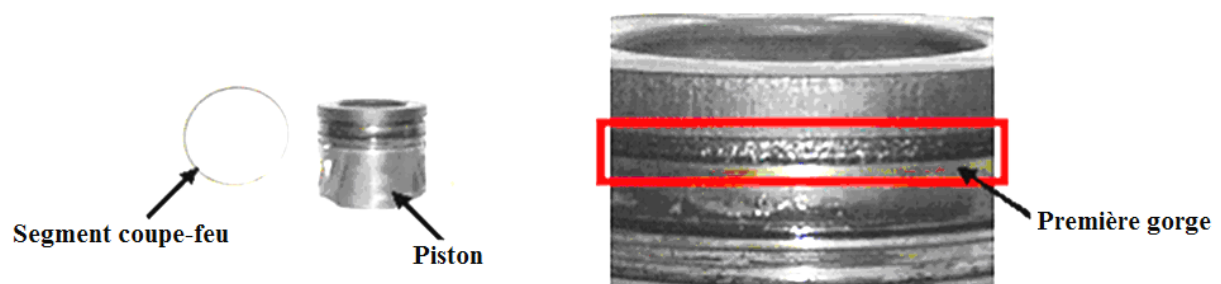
Photo du piston DW12B du test d'endurance de 200h
